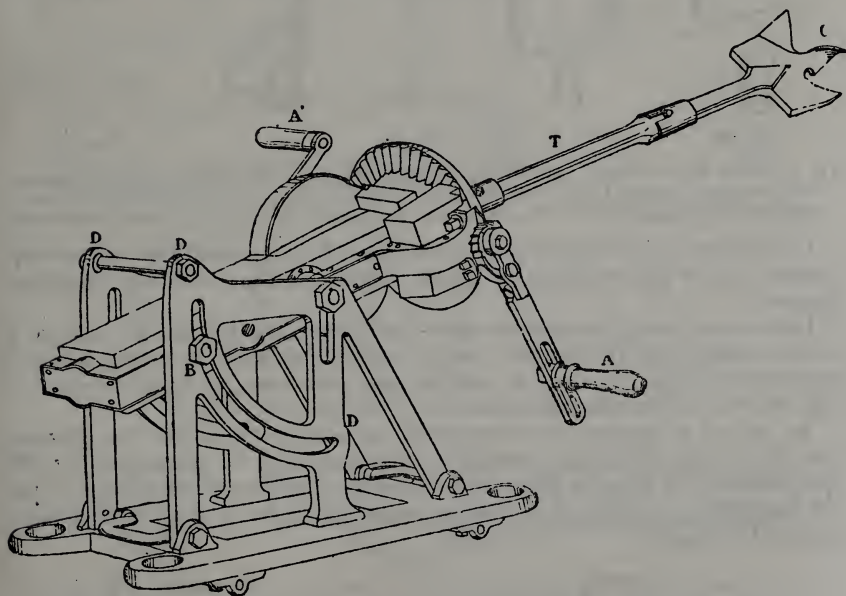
Machine à camouflets. Vue perspective, échelle 1/20.
